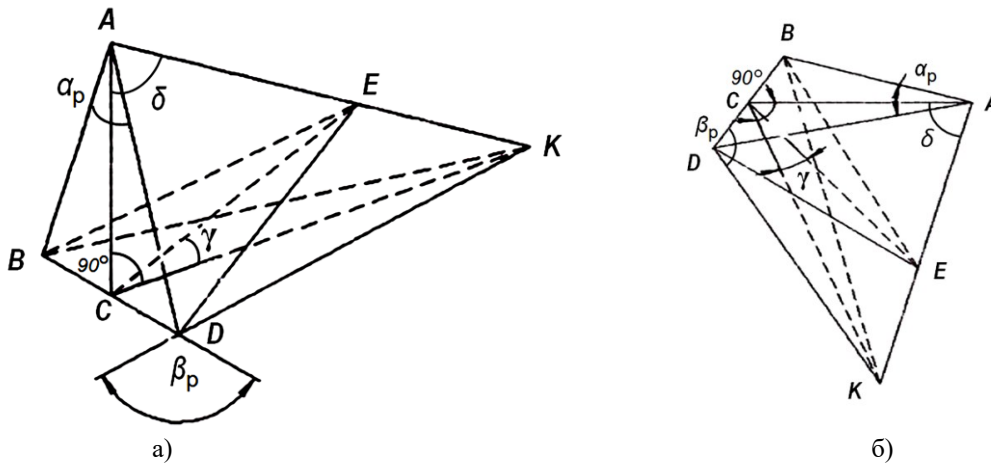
Робоча частина алмазного різця: а) зручний для розрахунків вигляд; б) робоче положення різця
